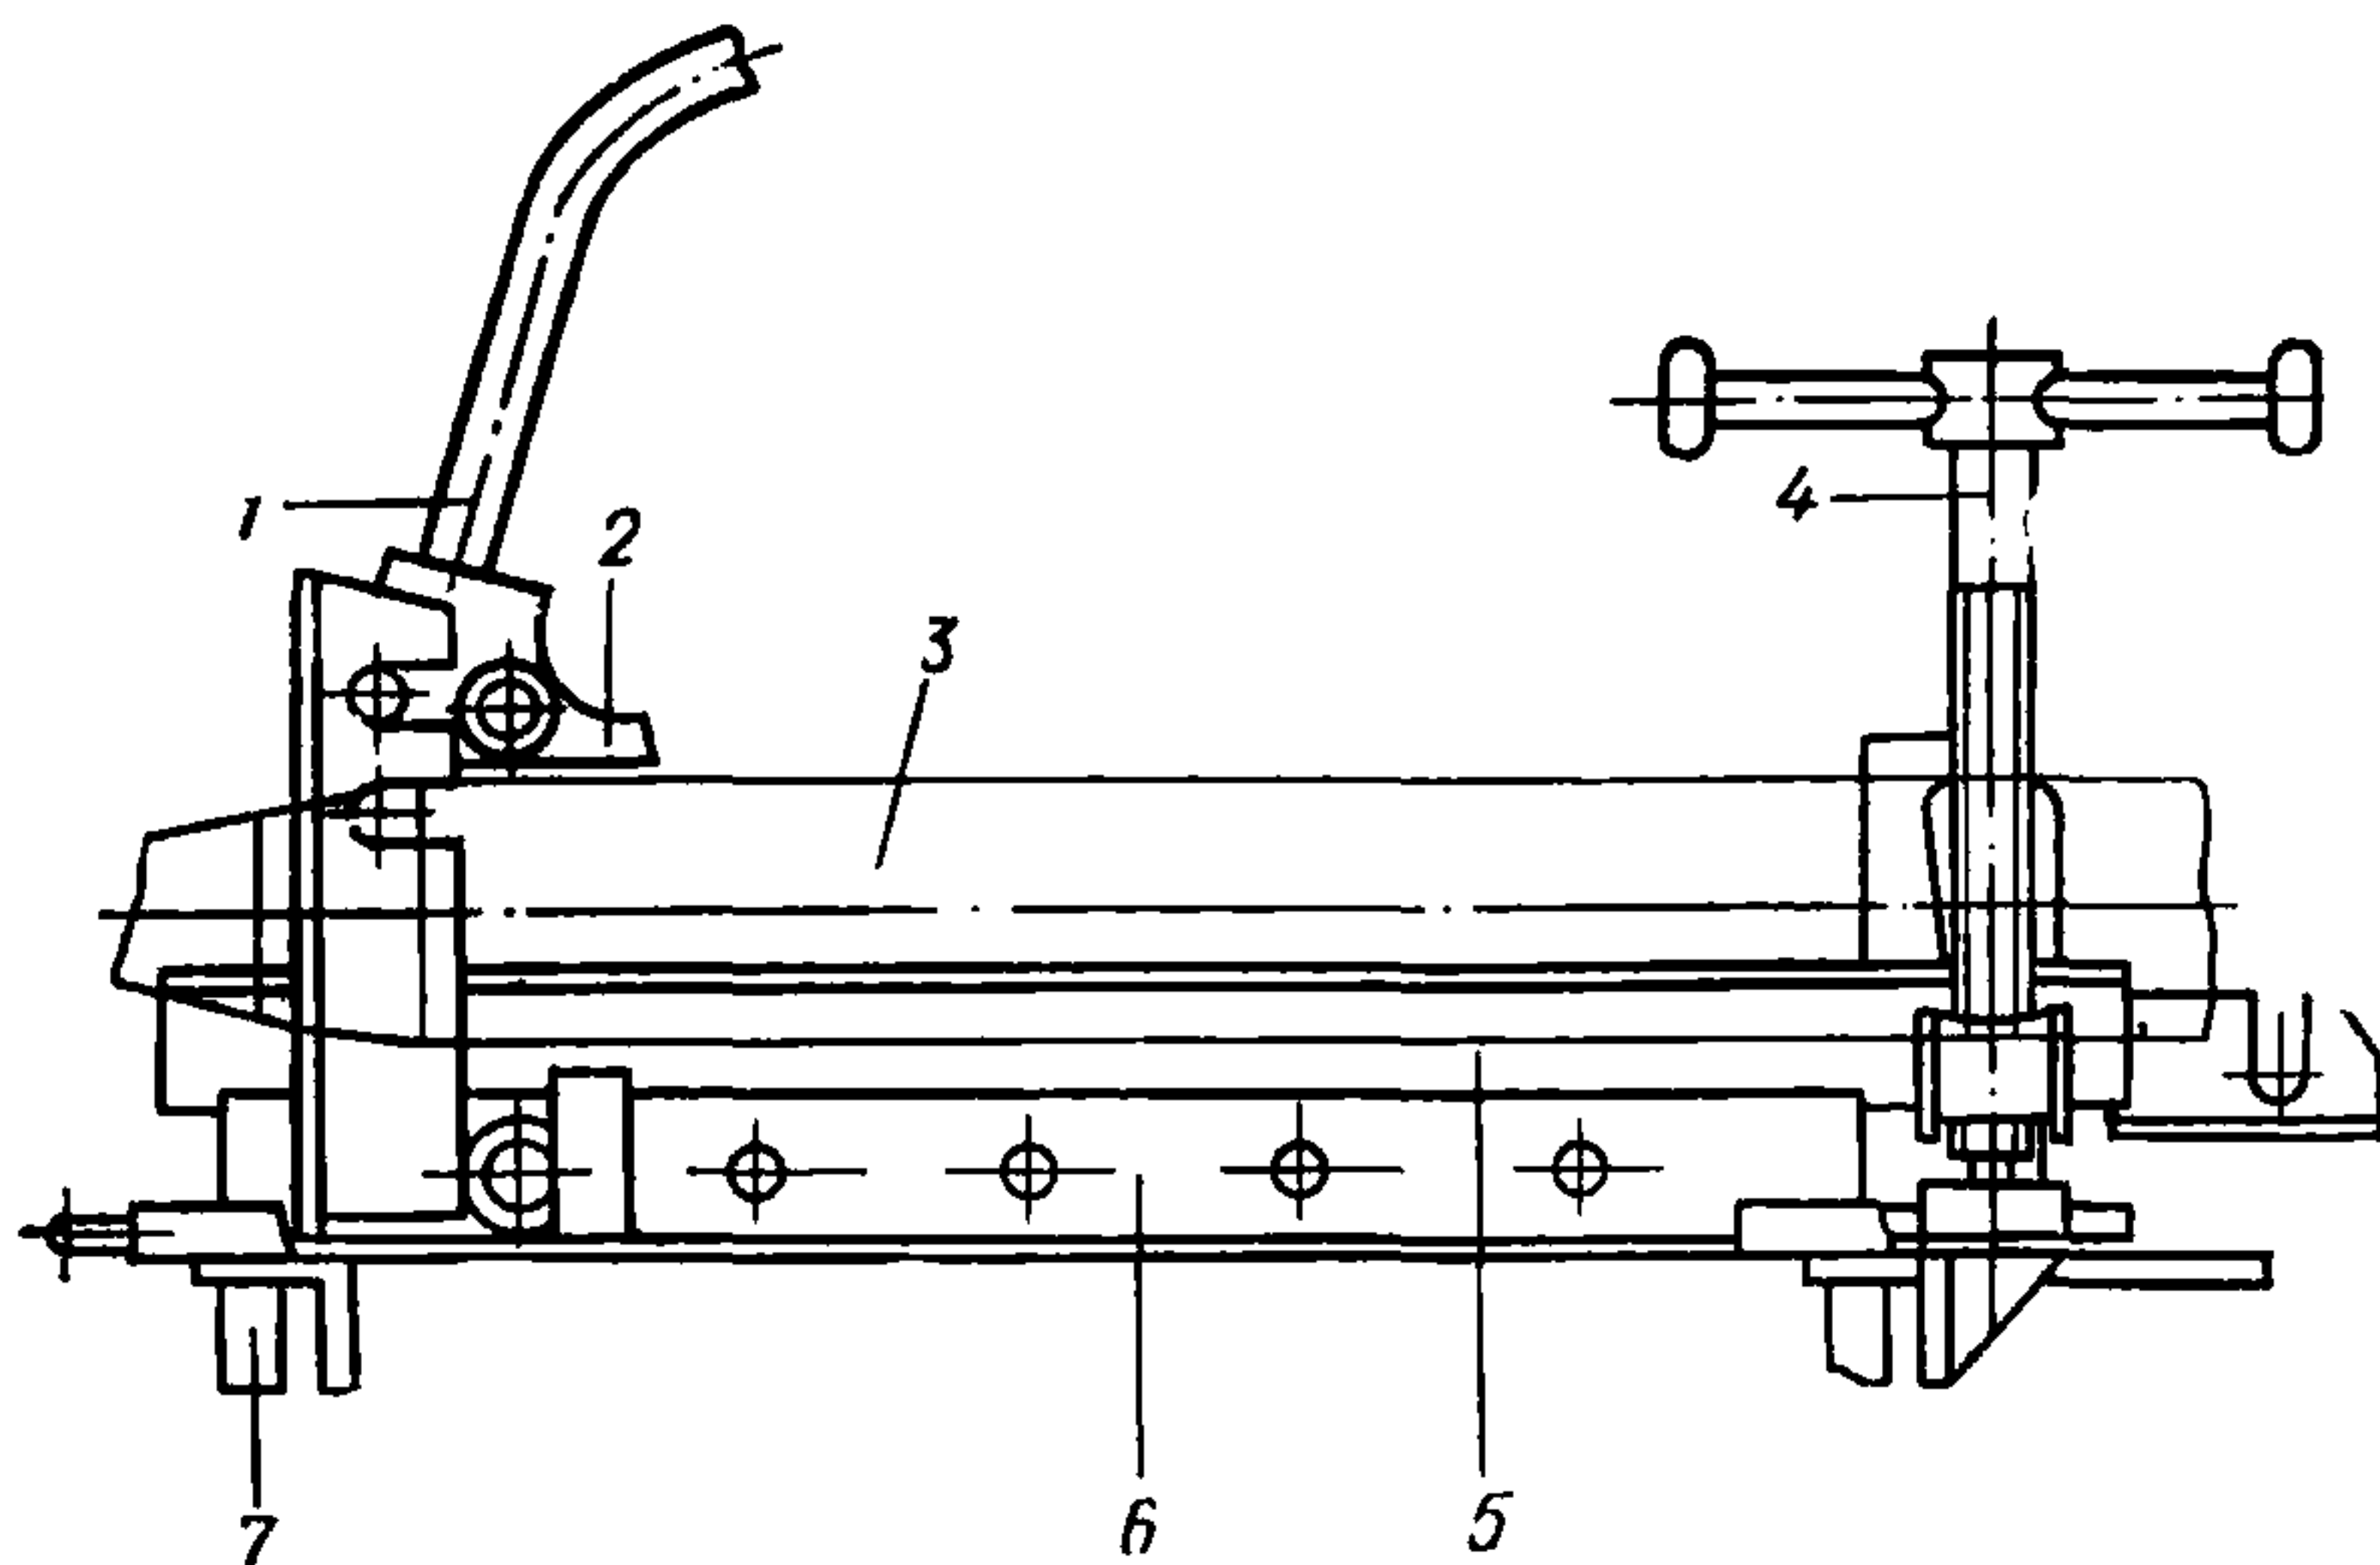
Схема стартового устройства для пневмопробойников ИП-4603 и ИП-4605
